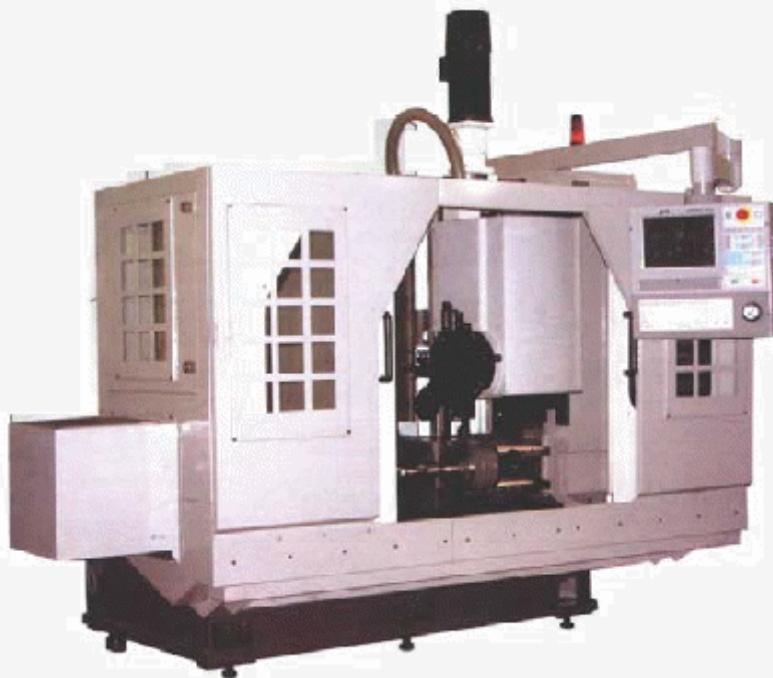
Станок токарный с ЧПУ модели 500 Т
